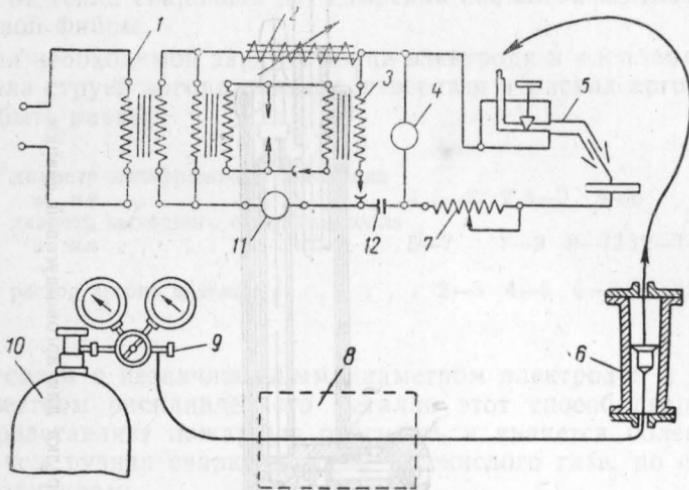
Схема установки для аргоно-дуговой сварки на переменном токе
